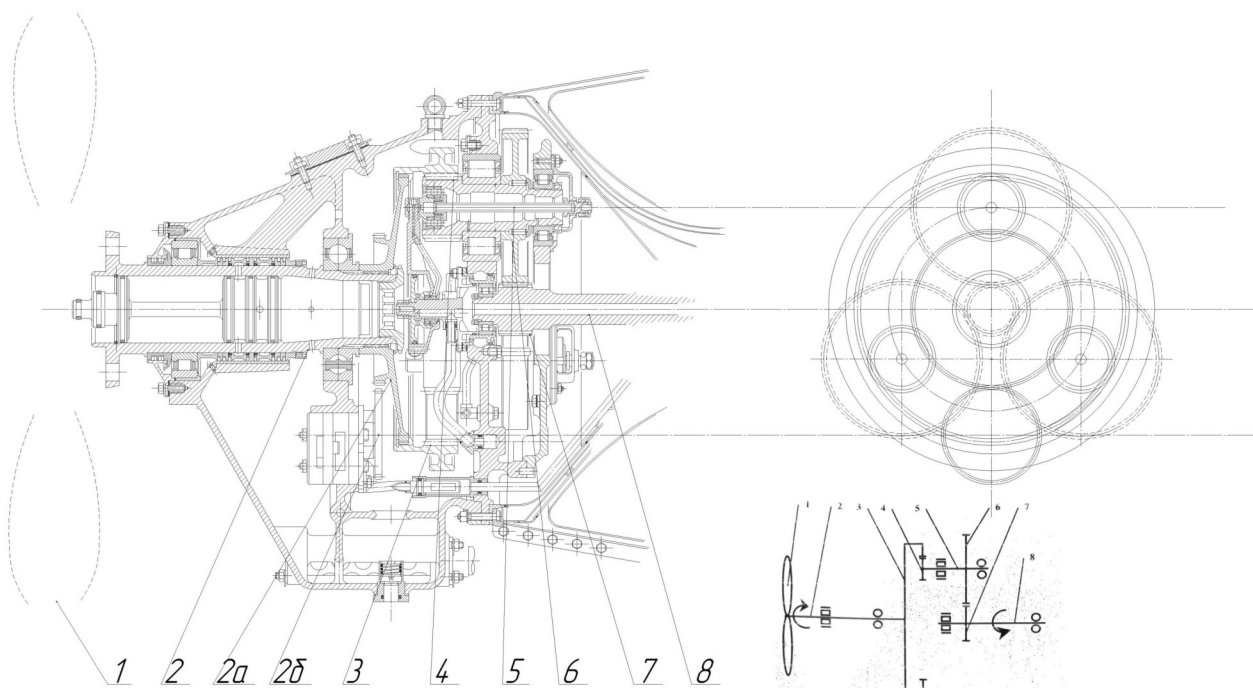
Псевдопланетарный двухступенчатый редуктор ТВД М601
